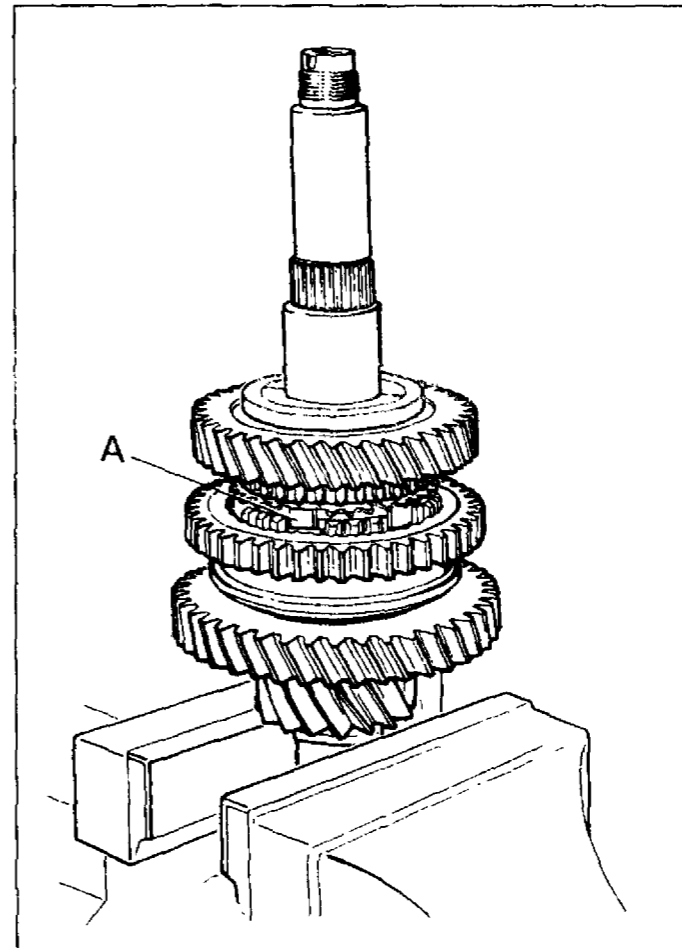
Установка синхронизатора I и II передач и ведомой шестерни II передачи
